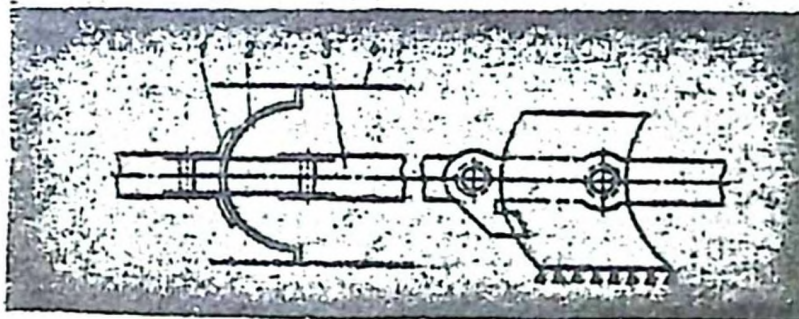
Новый рабочий орган скребкового транспортера:
